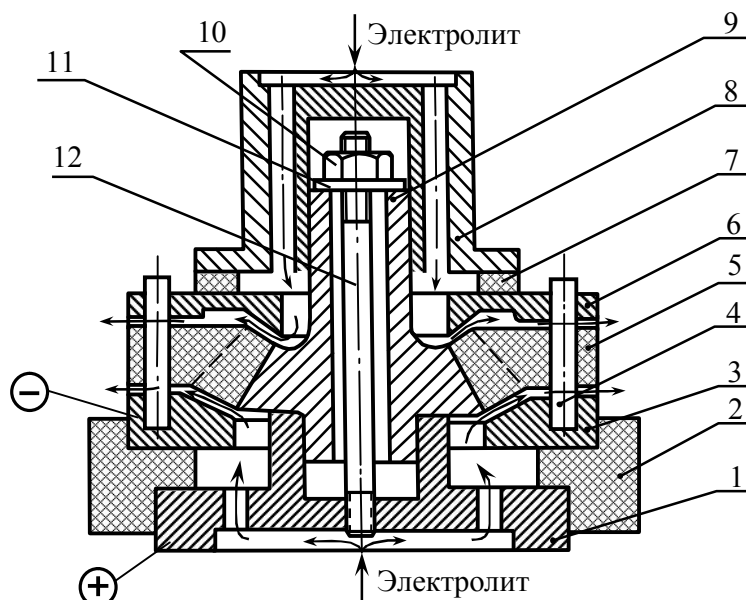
Схема приспособления для закругления острых кромок по торцам зуба у конического зубчатого колеса:
